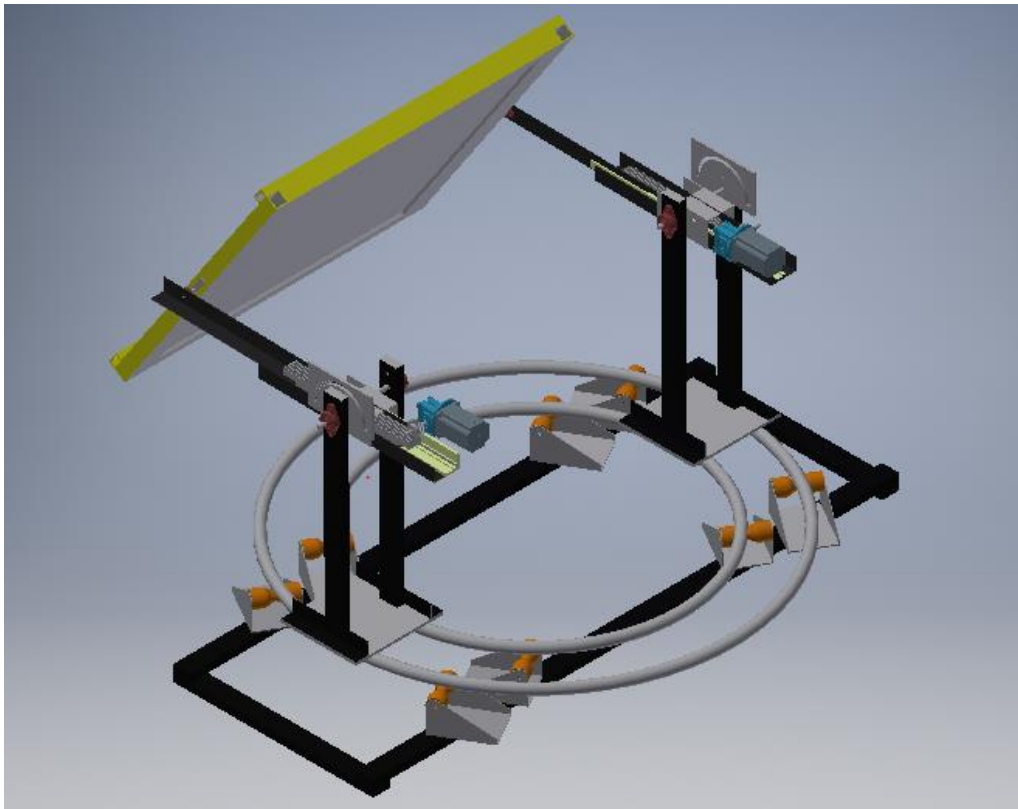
Modelo CAD de diseño definitivo de mecanismo. Elaboración propia.
